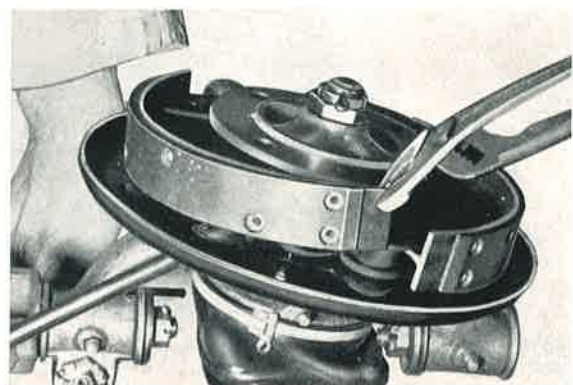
/2: Beide Bremsbacken vom Stützlager abheben.
